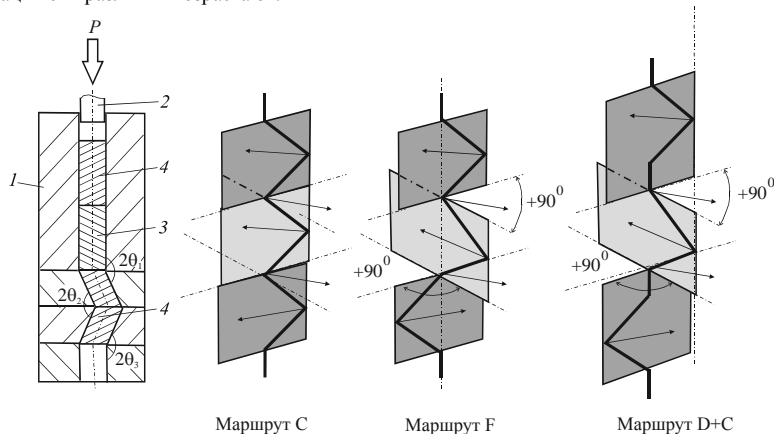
Схемы процесса и маршрута РКУЭ: 1- матрица, 2 – плунжер, 3 – полимерная заготовка, 4 – фальш-заготовка.
